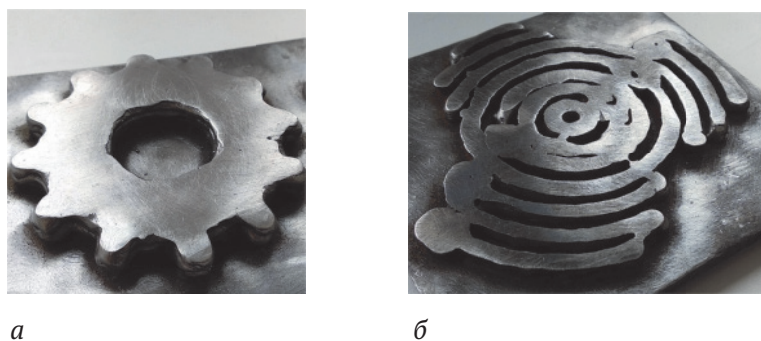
Наплавленная форма зубчатого колеса (а) и «прерывистой спирали» (б).
